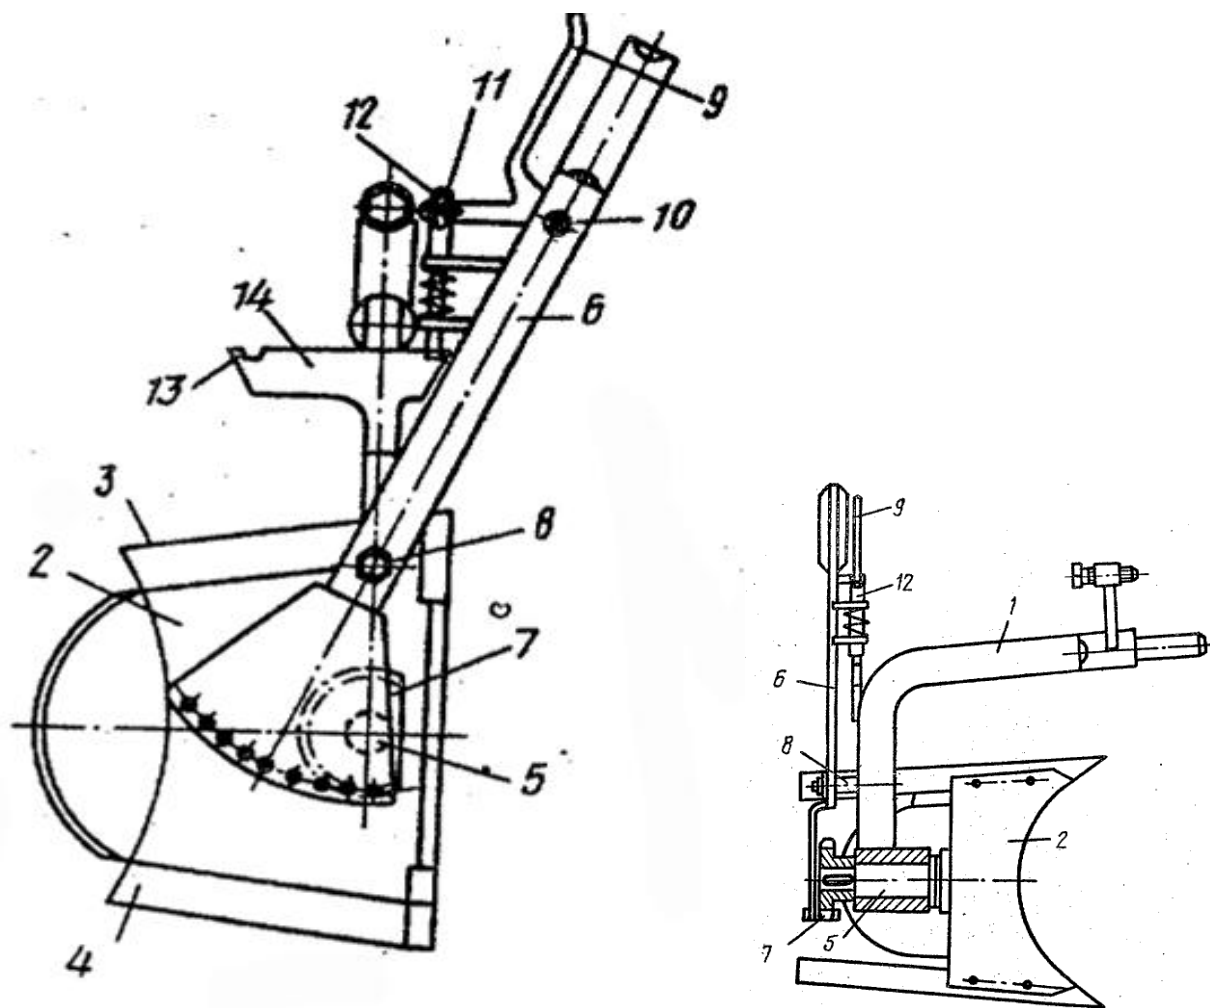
Корпус плуга до ручного мотоплуга [18]
